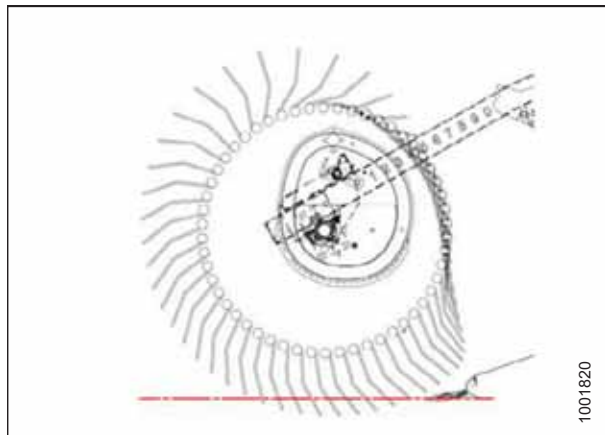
Вертикальний розріз пальця — положення 2
